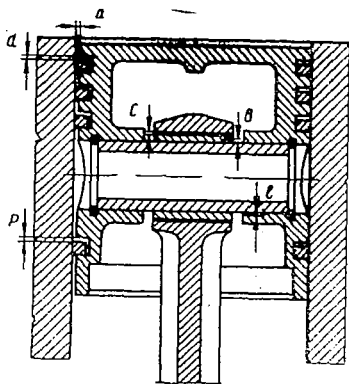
Схема сборки поршня и шатуна в цилиндре
